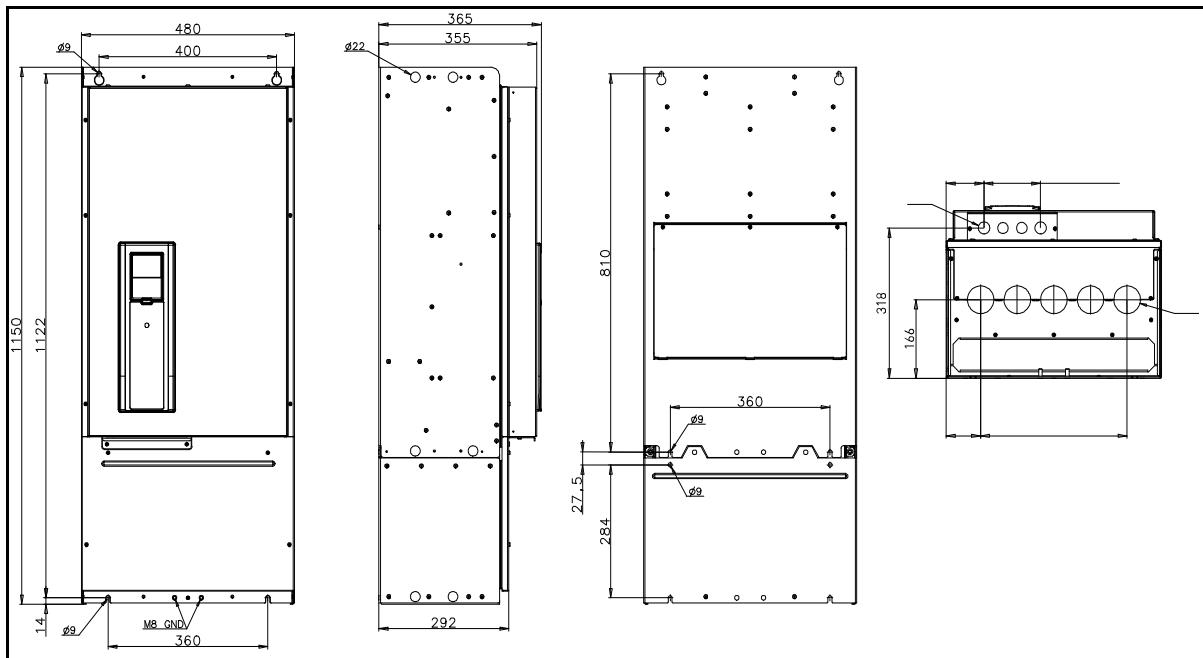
Dimensões do inversor de CA Vacon, MR9 IP21 e IP54
